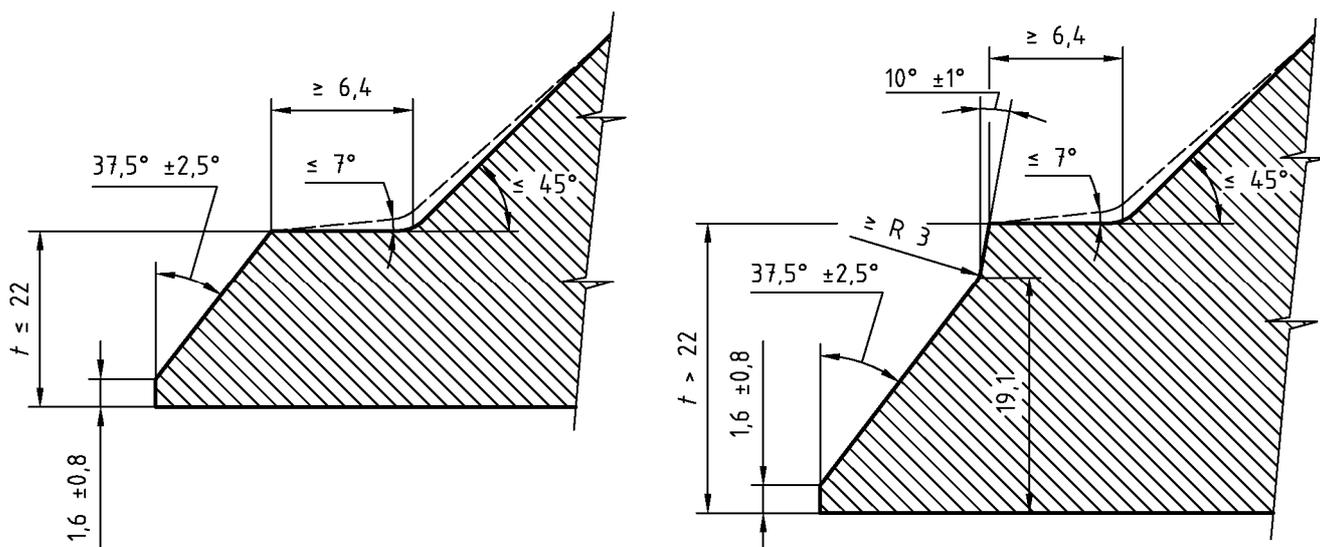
Разделка кромок под сварку фланцев с шейкой для приварки типа 6В и 6ВХ
